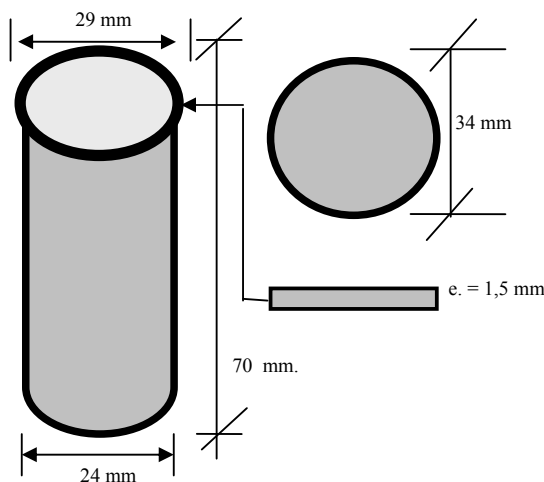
Dimensiones de la cápsula y tapa de aluminio.
